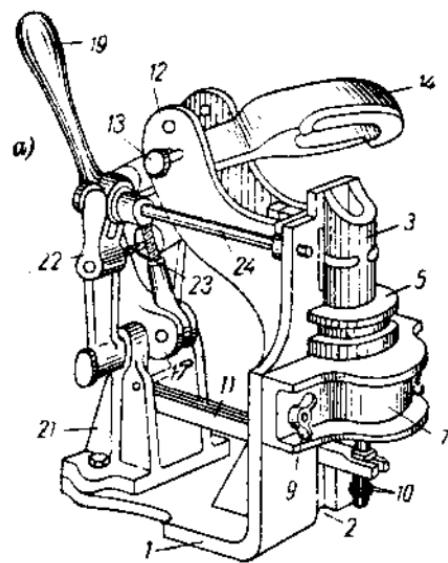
Прибор «Хемпи-Купер Н-60» для заливки подшипников.
